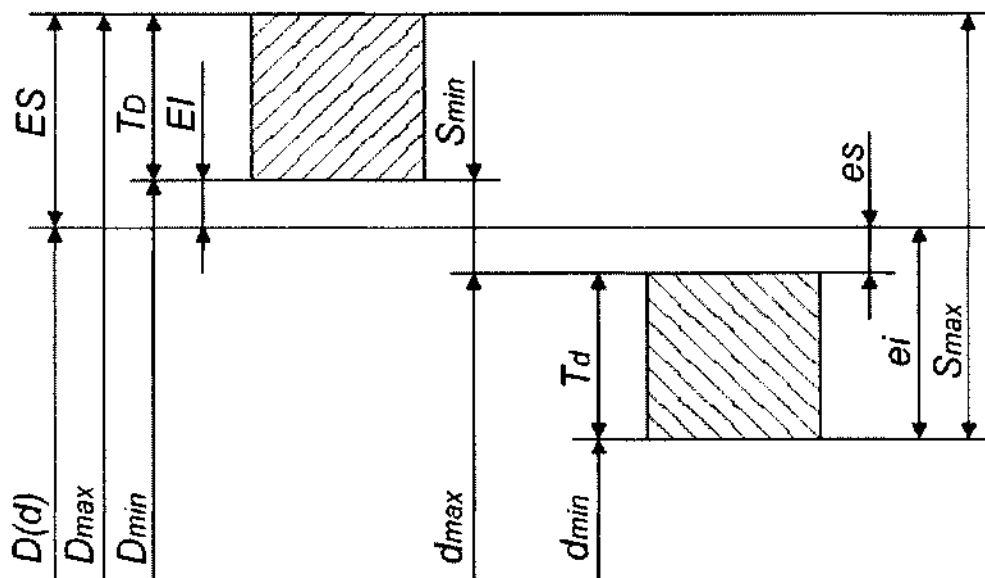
Схема расположения полей допусков отверстия и вала в посадках с зазором
